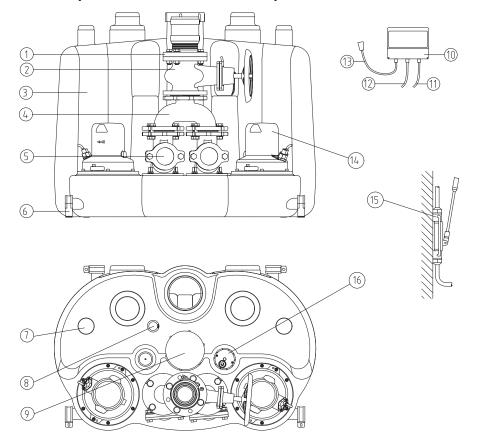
Struttura della postazione di sollevamento per materia fecale Sanimat 2002
